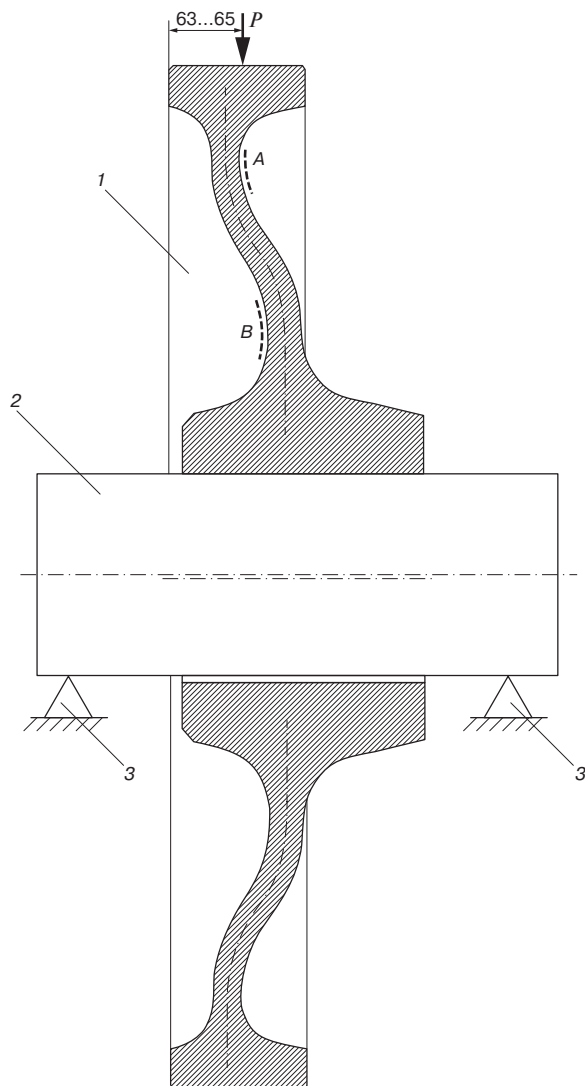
Типовая схема усталостного испытания катаного центра: 1 — центр; 2 — ось; 3 — неподвижные опоры
